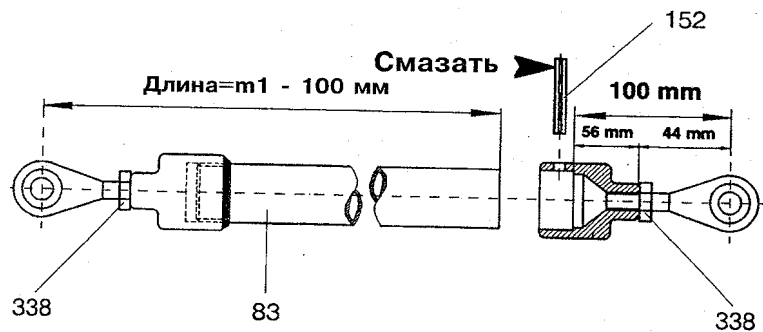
Установка приводного механизма заземлителя, раздельная установка. Приводной механизм с боковым смещением
